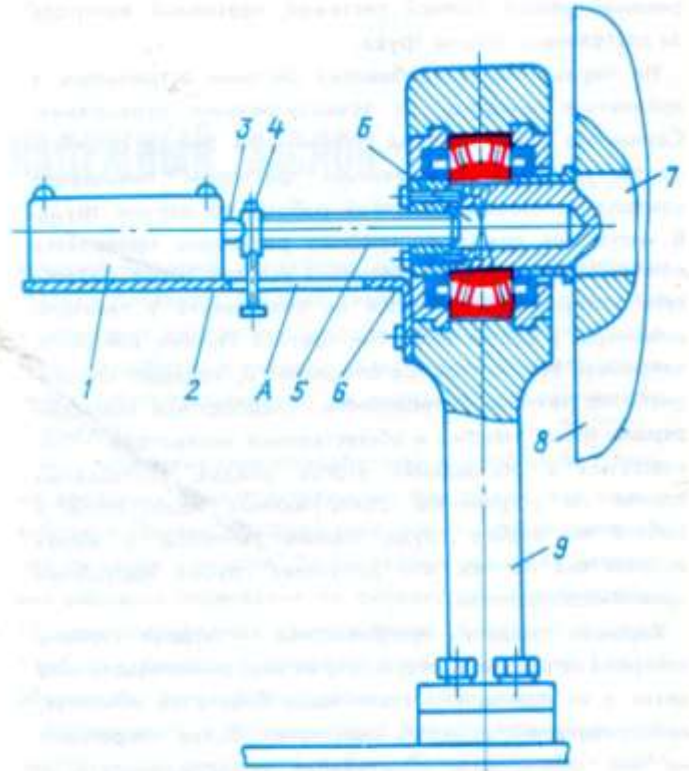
Новая конструкция ограничителя высоты подъема крюковой обоймы автомобильного крана: 1 — конечный выключатель; 2 — кронштейн; 3 — шток конечного выключателя; 4 — поводок; 5 — винт; 6 — гайка; 7 — вал; 8 — барабан; 9 — опора; А — продольный паз кронштейна; Б — цилиндрическая полость
